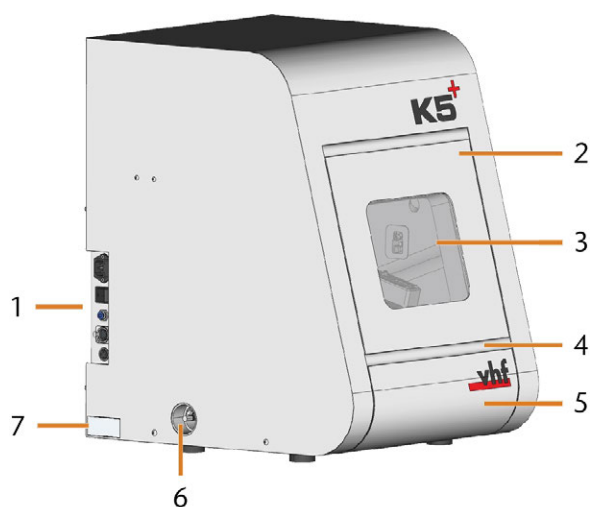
LATO ANTERIORE DELLA MACCHINA
